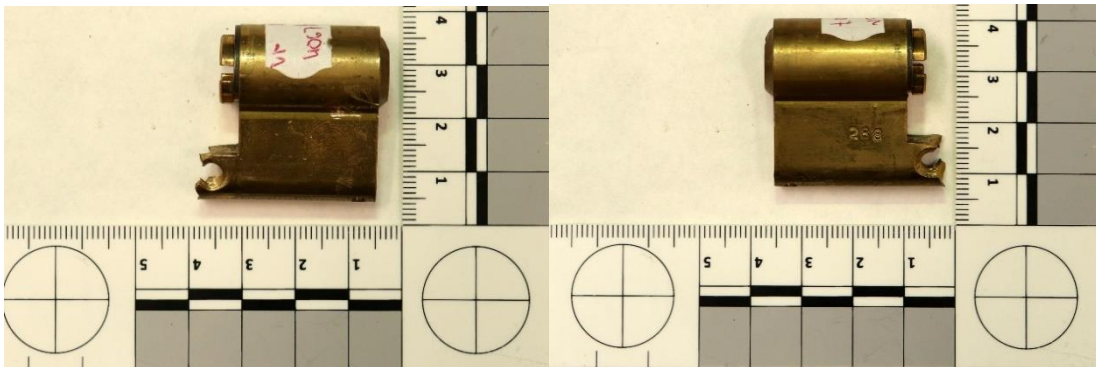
, 55, Detailní pohled na zanechané stopy, levá a pravá strana, Zdroj: vlastní
